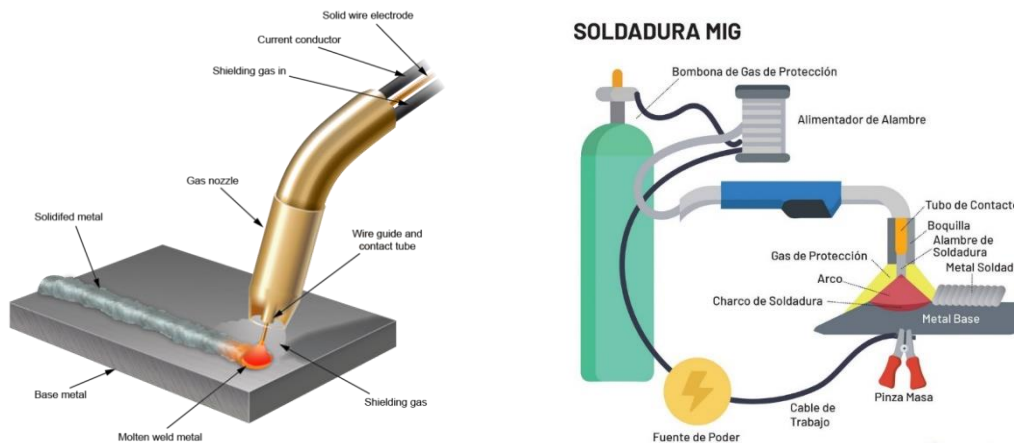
Soldadura GMAW (MIG/MAG)
